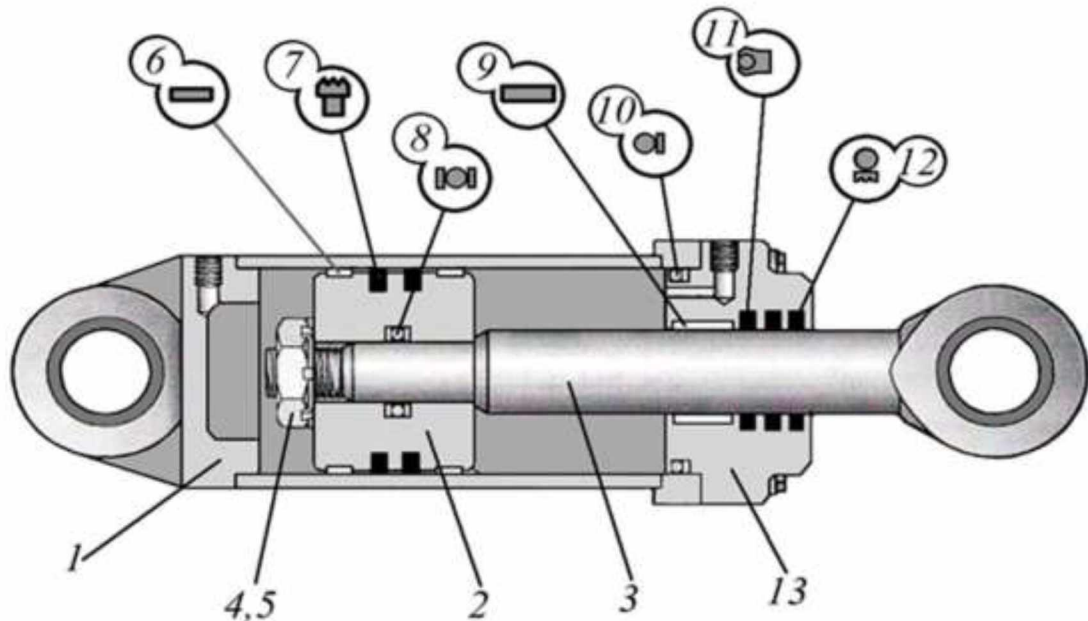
Типова конструкція поршневого гідроциліндра двосторонньої дії з одностороннім штоком: 1 - корпус (кришка задня з гільзою); 2 - поршень; 3 - шток; 4, 5 - гайки зі стопорною шайбою; 6 - напрямні кільця поршня; 7 - комбіновані ущільнення поршня 2; 8 - ущільнення з'єднання штока з поршнем; 9 - направляюче кільце штока; 10 - ущільнення з'єднання корпусу з передньою кришкою; 11 - комбіновані ущільнення штока; 12 - брудознімач; 13 - кришка передня
